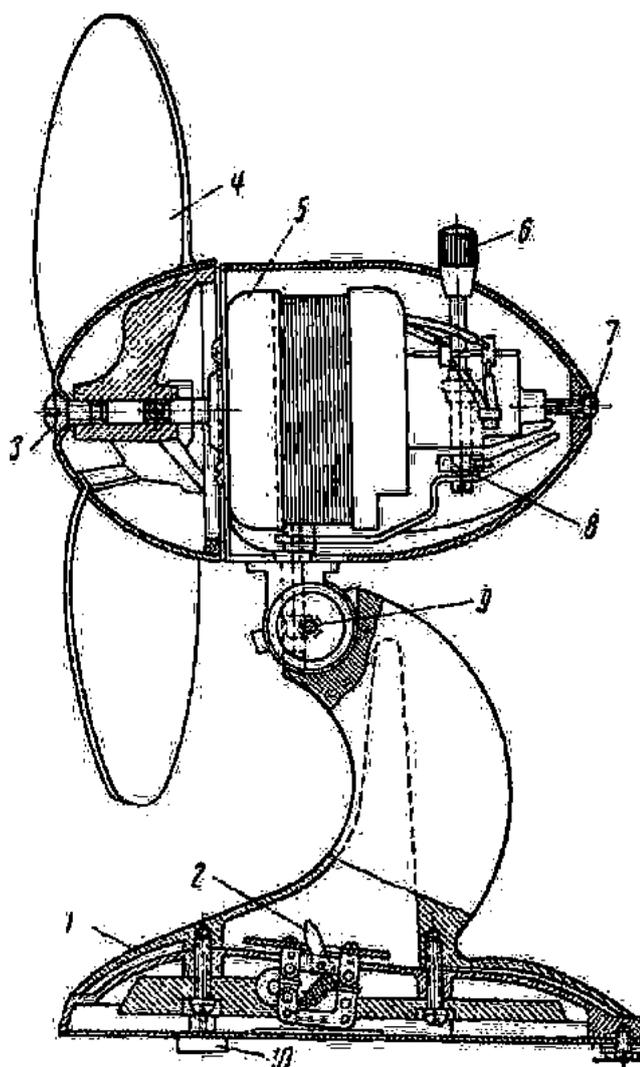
Вентилятор ВЭ-1: 1 - стойка; 2 - выключатель; 3 - винт крепления колпака с резиновыми лопастями; 4 - крыльчатки с резиновыми лопастями; 5 - электродвигатель; 6 - ручка стопорного валика; 7 - винт крепления кожуха электродвигателя; 8 - червячный редуктор; 9 - шарнирное крепление; 10 - резиновая подставка
